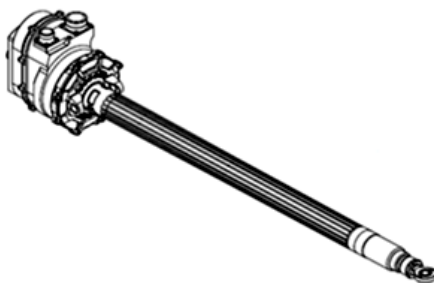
Внешний вид электромеханизма реверсивного устройства
